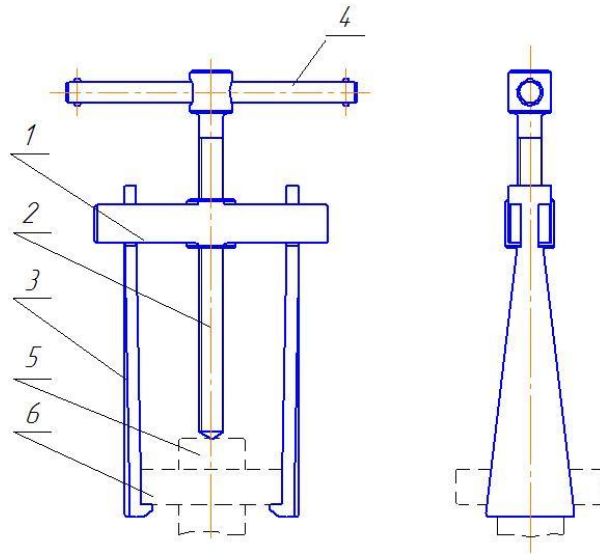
Знімач з циліндричними лапами для демонтажу з валів деталей, встановлених з натягом: 1 – траверса; 2 – силовий гвинт; 3 – захоплюючі лапи; 4 – важіль; 5 – вал; 6 – деталь, що знімається.
